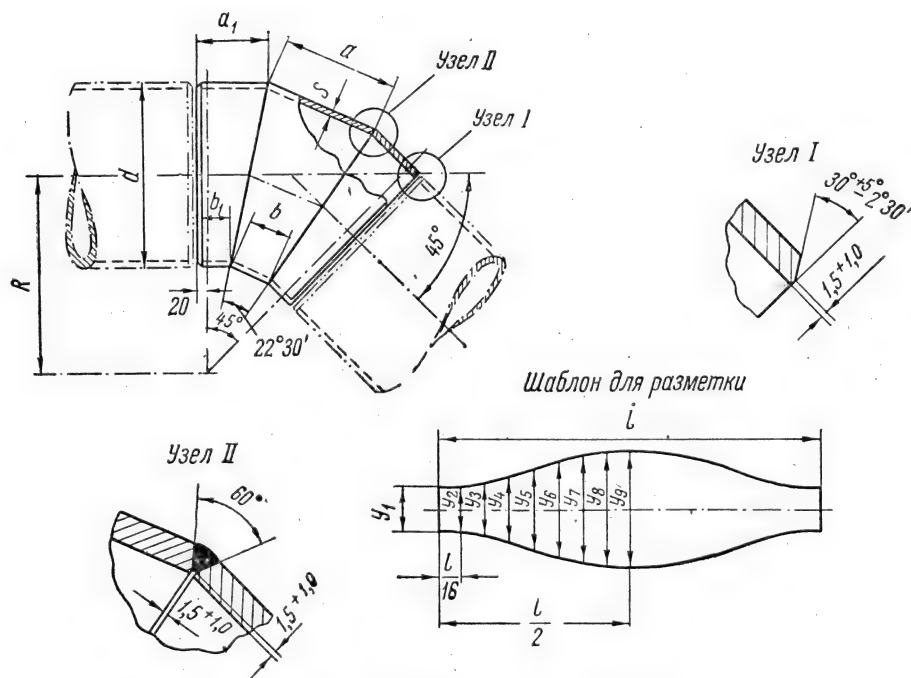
Отвод сварной с углом поворота 45° .
